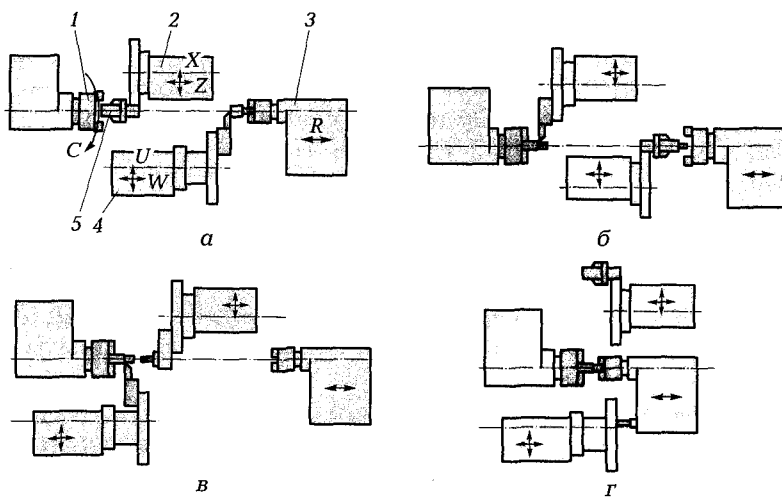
Последовательность обработки заготовки на станке с двумя револьверными головками и противошпинделем:
